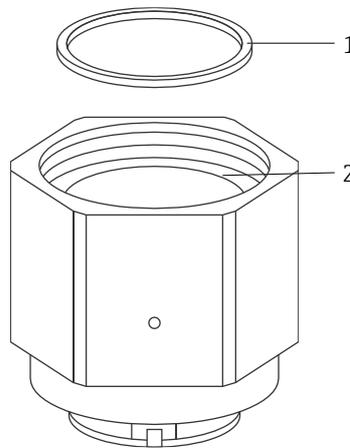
Centrage du joint sur la surface d'étanchéité du capuchon
